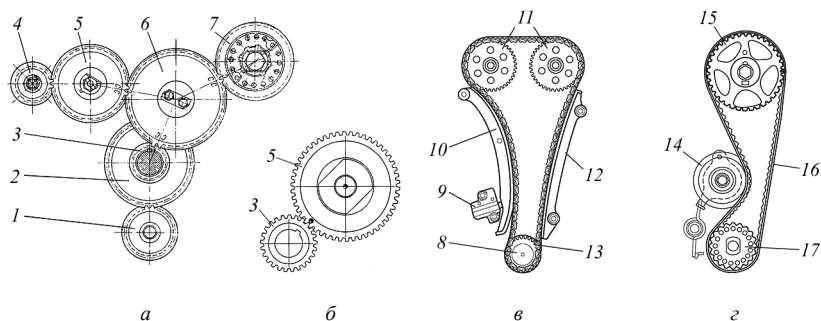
Типы привода распределительного вала: а – зубчатый дизельного двигателя; б – зубчатый бензинового двигателя; в – цепной; г – ременный; 1 – ведомая шестерня привода масляного насоса; 2 – ведущая шестерня привода масляного насоса; 3 – шестерня коленчатого вала; 4 – шестерня привода масляного насоса гидроусилителя руля; 5 – шестерня распределительного вала; 6 – промежуточная шестерня; 7 – шестерня привода топливного насоса; 8 – звездочка коленчатого вала; 9 – натяжитель цепи; 10 – башмак натяжителя; 11 – звездочка распределительного вала; 12 – успокоитель; 13 – цепь; 14 – натяжной ролик; 15 – шкив распределительного вала; 16 – зубчатый ремень; 17 – шкив коленчатого вала
